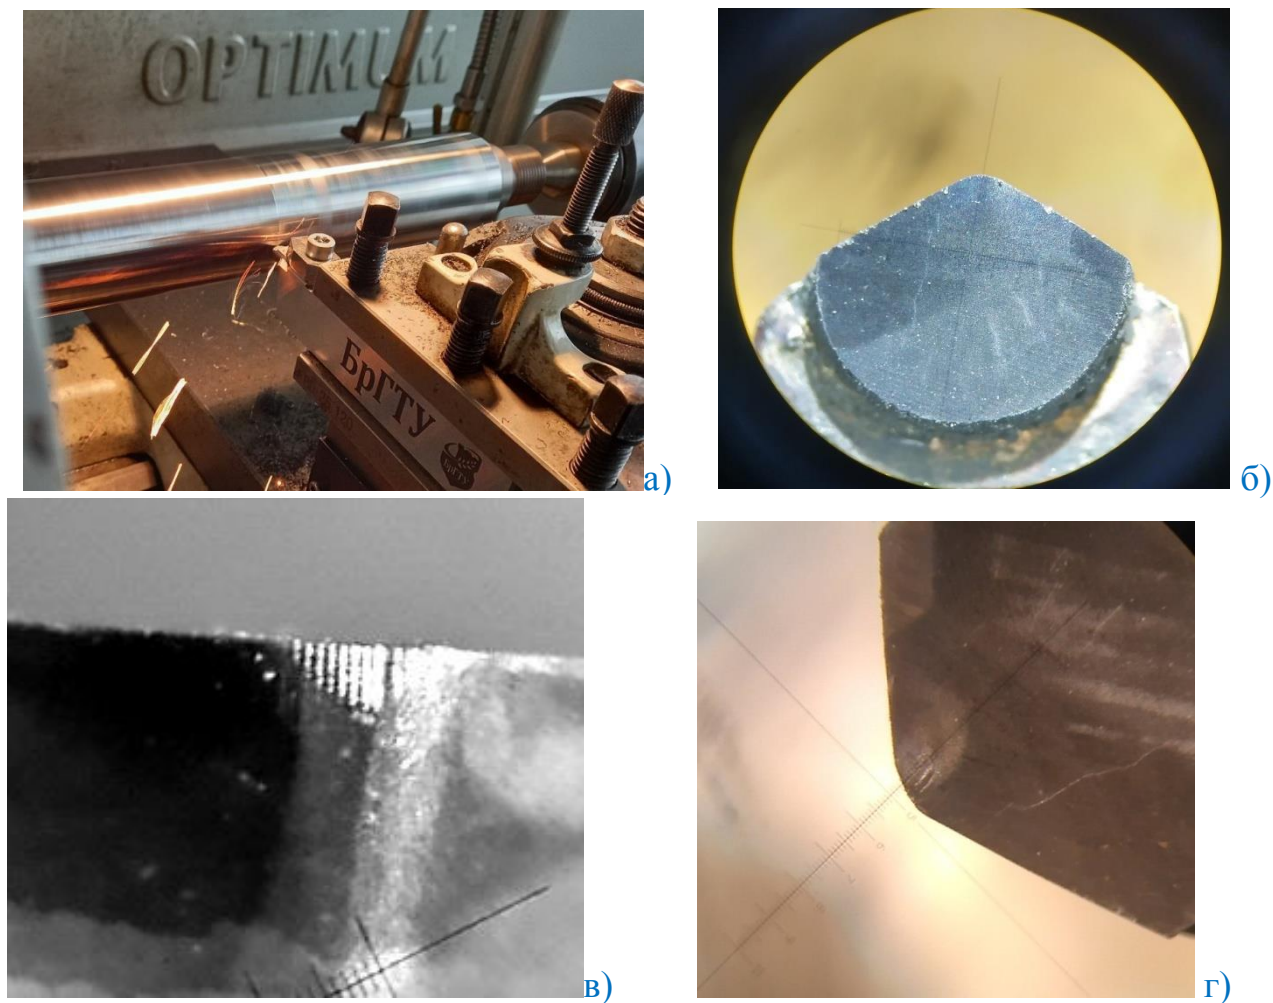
Экспериментальные исследования: а) наружное точение штока прямым проходным резцом; б) режущая часть резца с напаянной вставкой из композита cBN–Al; в) износ вставки по задней поверхности; г) износ вставки по передней поверхности
